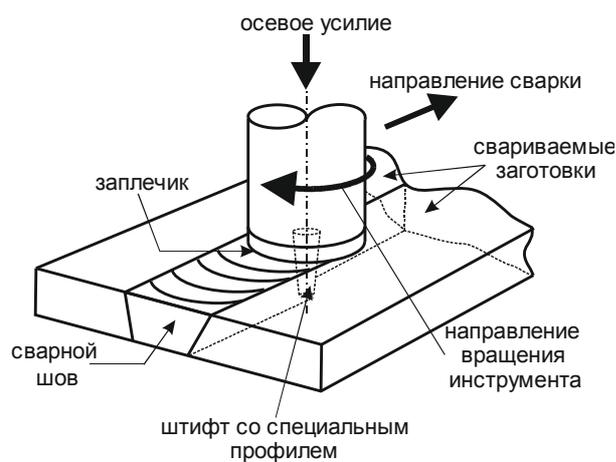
Схематичное изображение процесса сварки трением с перемешиванием
